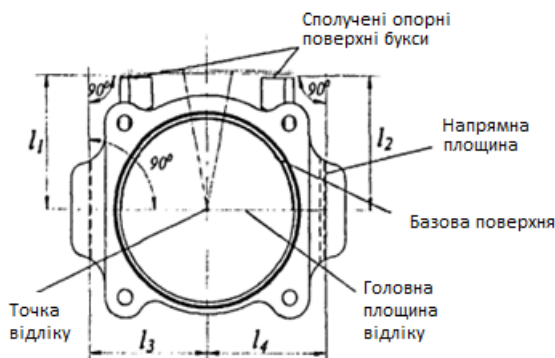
Схема основних поверхонь корпусу букси, що взаємодіють з боковою рамою візка 18-100
